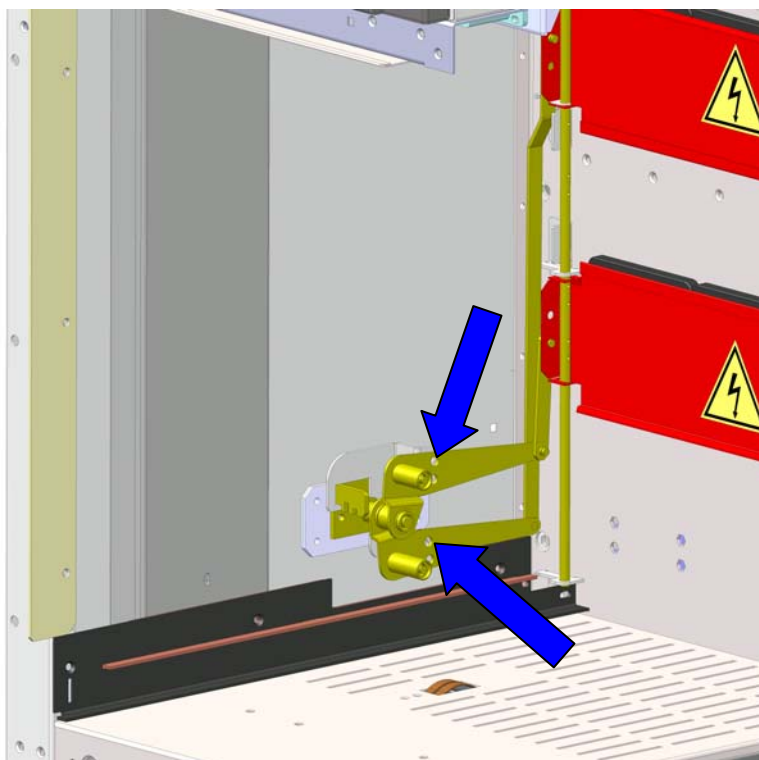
Места расположения отверстий для блокировки шторочного механизма в отсеке выкатного элемента
